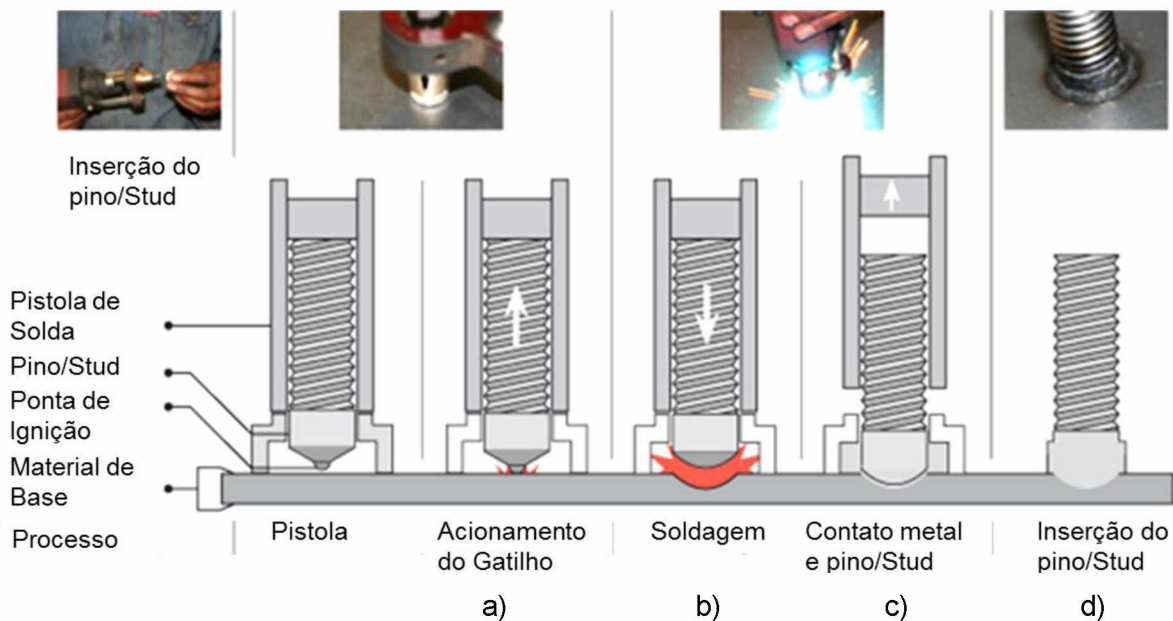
Sequência de deposição de pinos com o processo de soldagem por arco. (RIVET & WELDSTUD MANUFACTURING CC, 2015)
